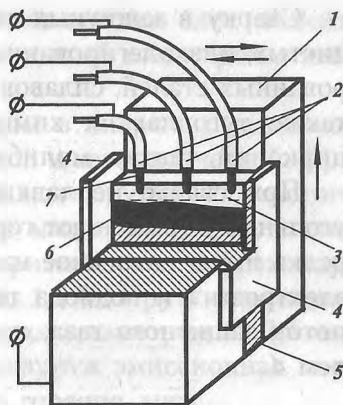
Схема электрошлаковой сварки: 1 — свариваемые детали; 2 — мундштук; 3 — расплавленный флюс; 4 — медные ползуны; 5 — шов; 6 — расплавленный металл; 7 — электрод
